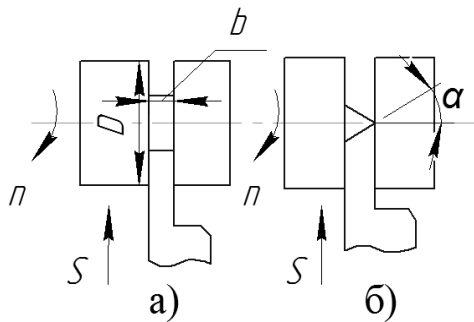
Відрізування заготовок на токарних верстатах різцями з прямими (а) і скошеними (б) різальними кромками
